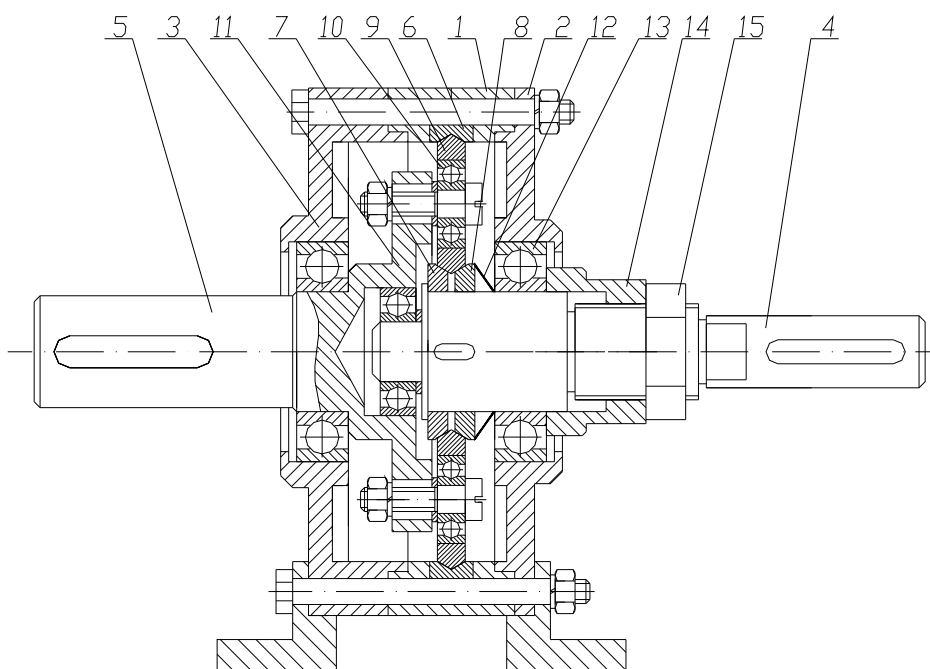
Фрикционная планетарная передача с подшипниками сателлитами
